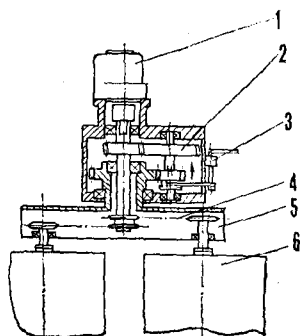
Рабочий орган машины для мойки обстановки пути: 1– гидромотор привода рабочих органов; 2– редуктор; 3–механизм переключения; 4– цепная передача; 5– коромысло; 6– щетка.
